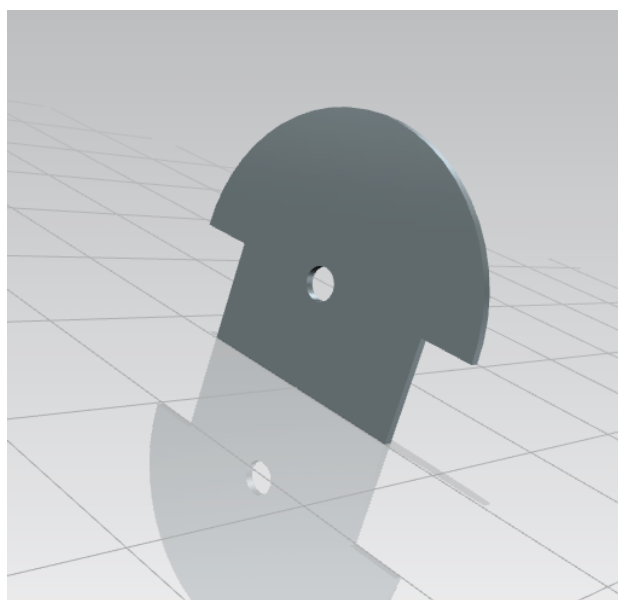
Развертка детали с фланцем и отбортовкой центрального отверстия
